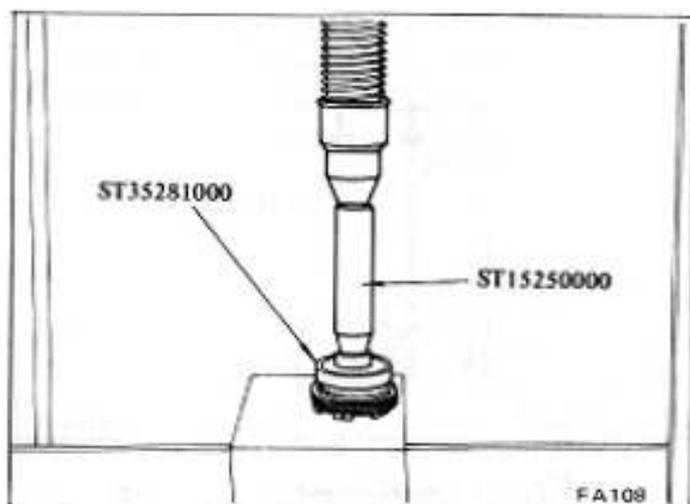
Mise en place du joint d'étanchéité de graisse
